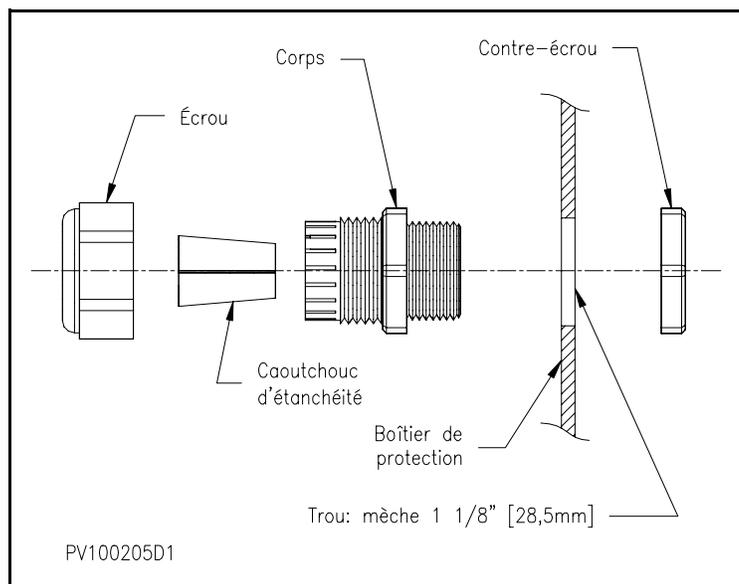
Installation d'un connecteur étanche de type presse-étoupe
